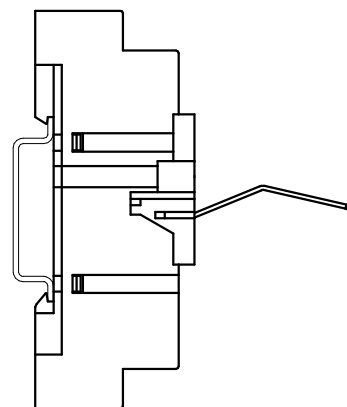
Розетка Р30 с креплением на DIN-рейку
